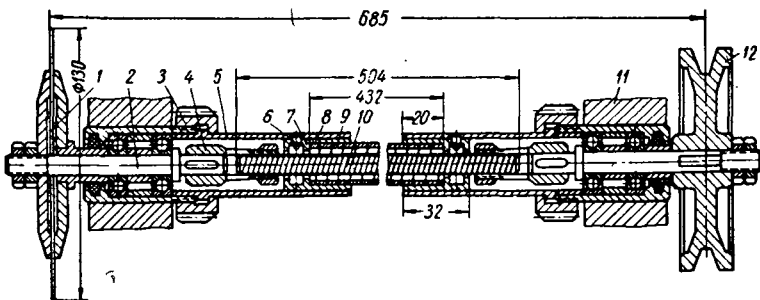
Привод отбора мощности с зубчатой передачей и универсальным шарниром:
